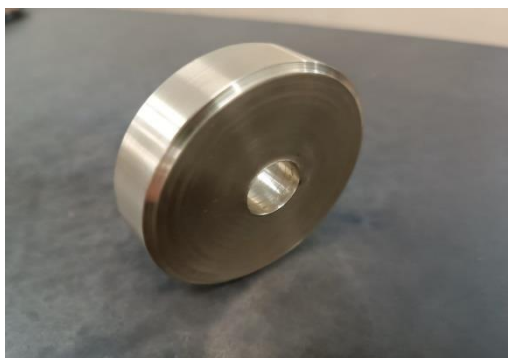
Engrenagem pronta para o processo de usinagem dos dentes
